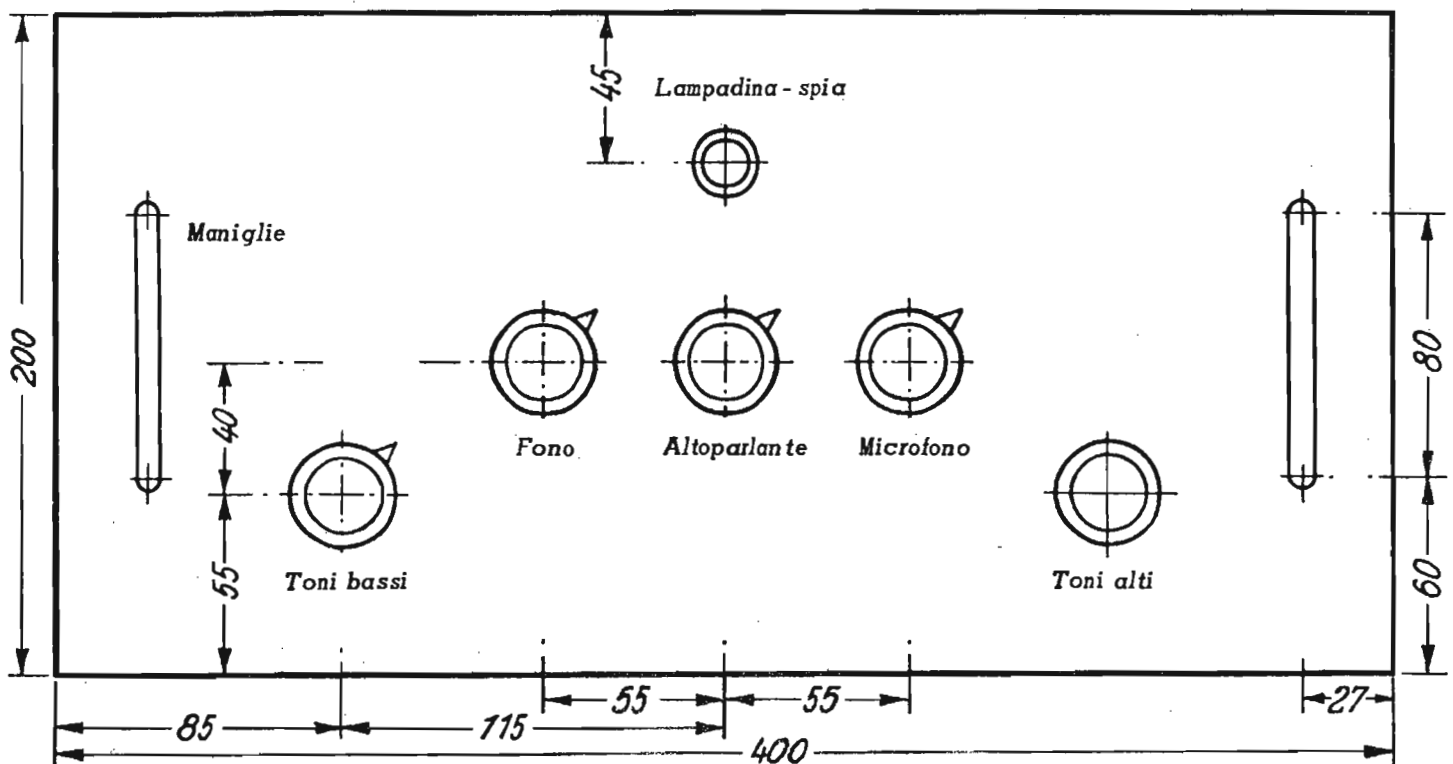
Disposizione delle singole parti sul pannello frontale.
